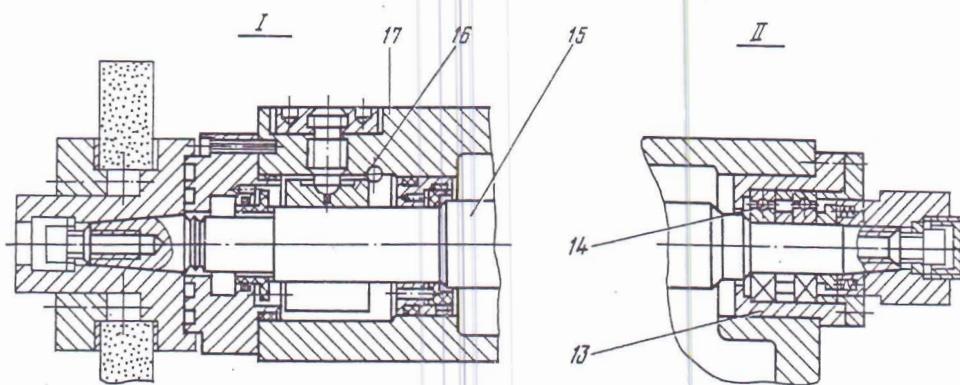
Шпиндель шлифовальной головки для станков ЗЕ711ВФ1, ЗЕ721АФ1-1, ЗЕ711АФ1,
